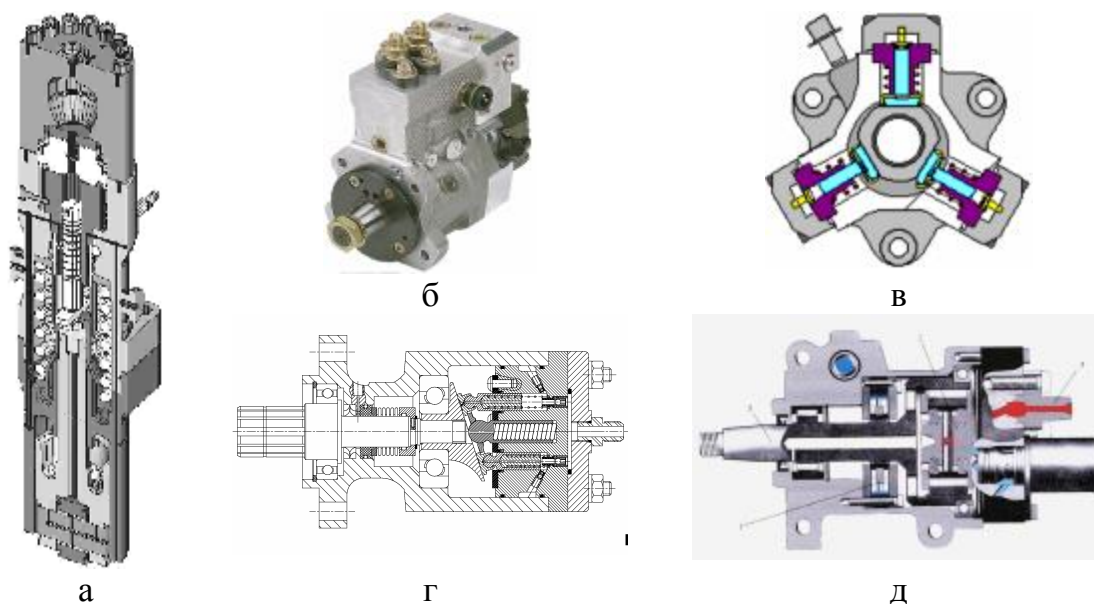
ТНВД для CR: а–индивидуальный Sulzer; б–рядный R.Bosch; в–радиально-плунжерный R.Bosch; г–аксиальный AVL; д–роторный Delphi
